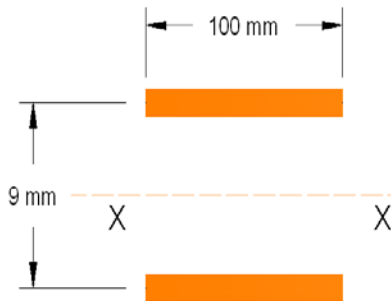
Geometría de la soldadura a realizar
